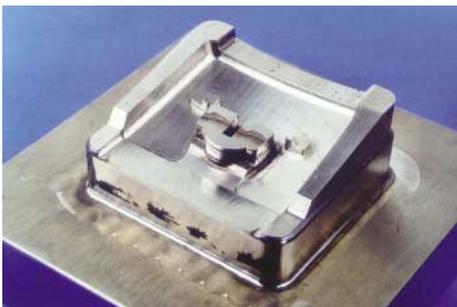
Gegenstück des SG-Werkzeugeinsatzes (auch mittels CMB gefertigt)
